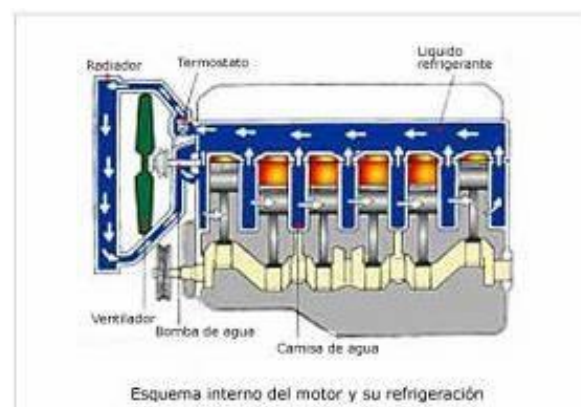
Partes de una Refrigeración mixta. Fuente: AUTOYTÉCNICA.COM [37]
